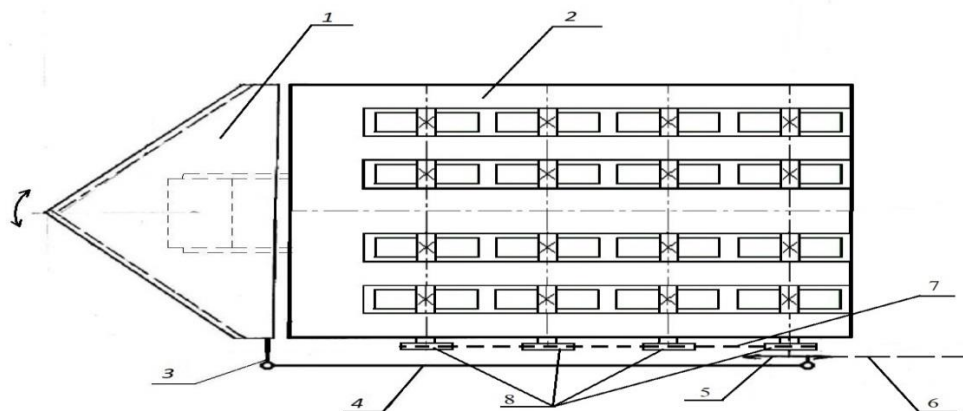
Схема подкапывающего лемеха с активной подрезающей частью и активной рабочей поверхностью.
